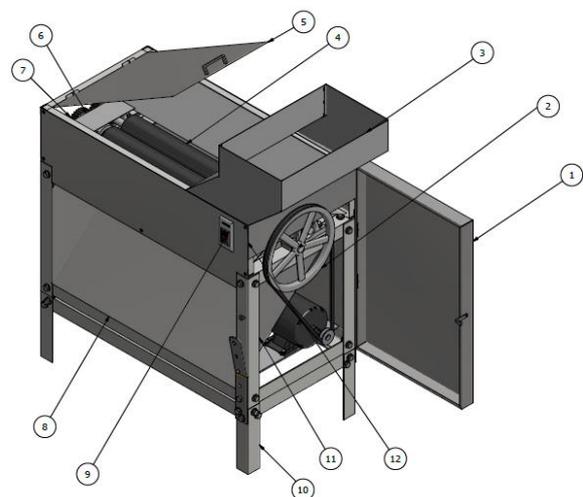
Máquina deshojadora de maíz, con el sistema de rodillos giratorios con caucho vulcanizado.
